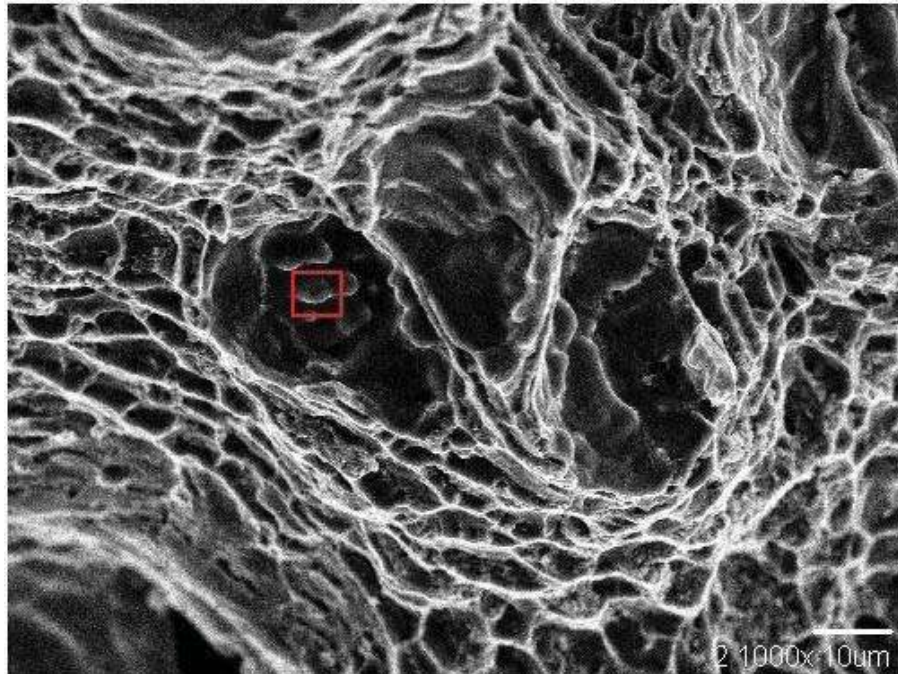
Análisis de la superficie de fractura de las soldaduras
